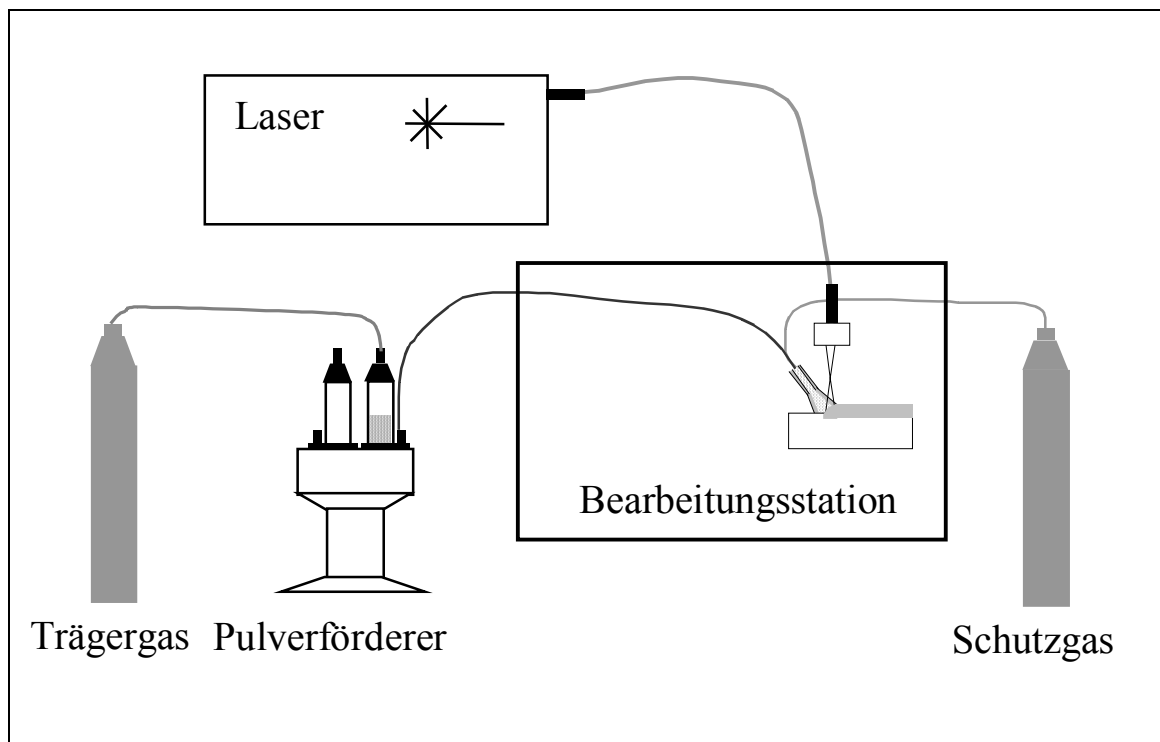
Gerätetechnik für das Laserbeschichten und das Laserschweißen
